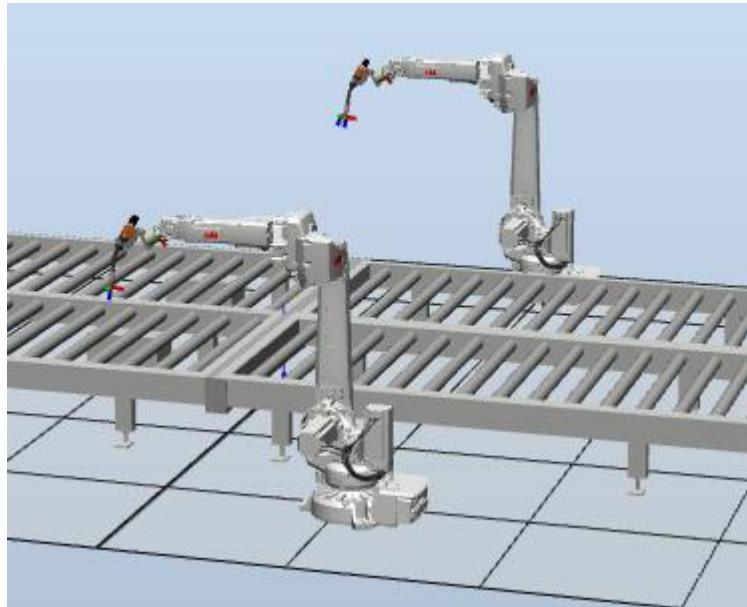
Sistemas robotizados destinados al proceso de soldadura.
